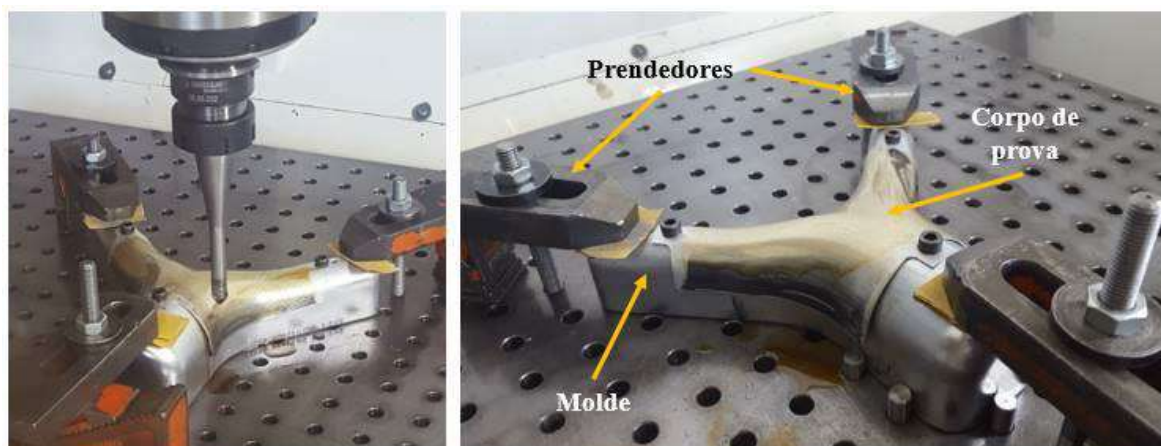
Conjunto corpo de prova e ferramental montados sobre a mesa da máquina fresadora.
